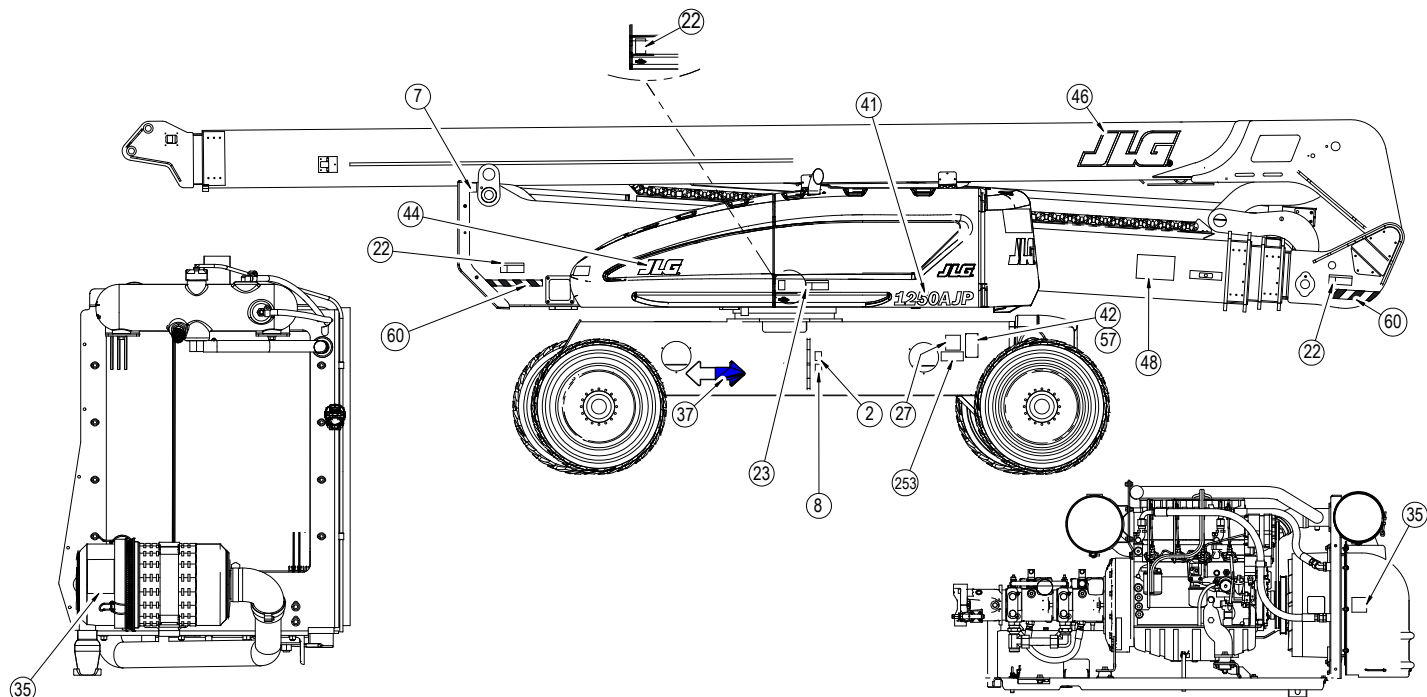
Dekalplacering - Serienummer 0300141446 till nu - Endast CE - Blad 4 av 5
